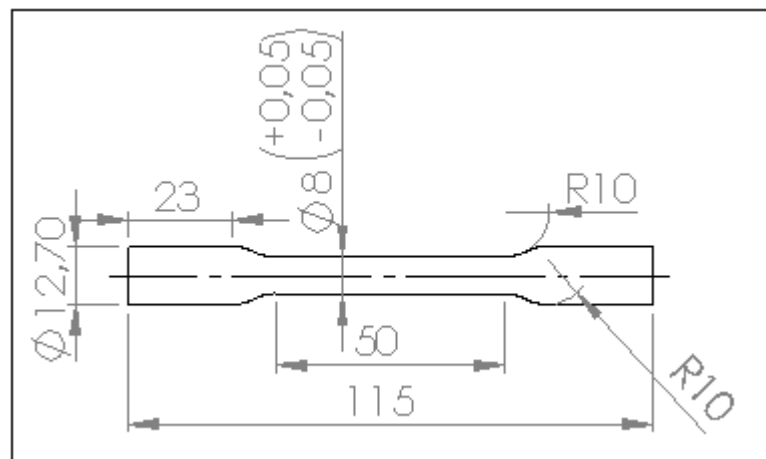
Dimensões básicas de corpo de prova usinado.
